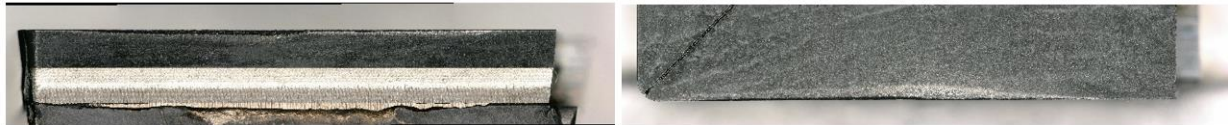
Poškození řezné hrany PCBN testu č. 10.1
